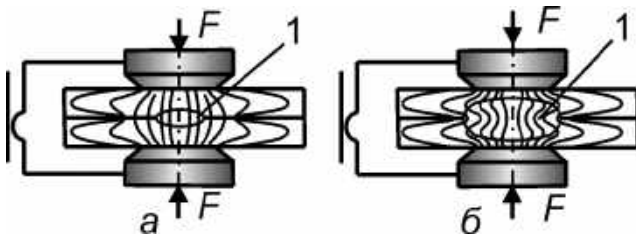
Схема ліній струму при точковому зварюванні: а – добре очищені деталі; б – деталі покриті окисами; 1 – лите ядро при однаковій тривалості нагрівання; F – зусилля стиснення
